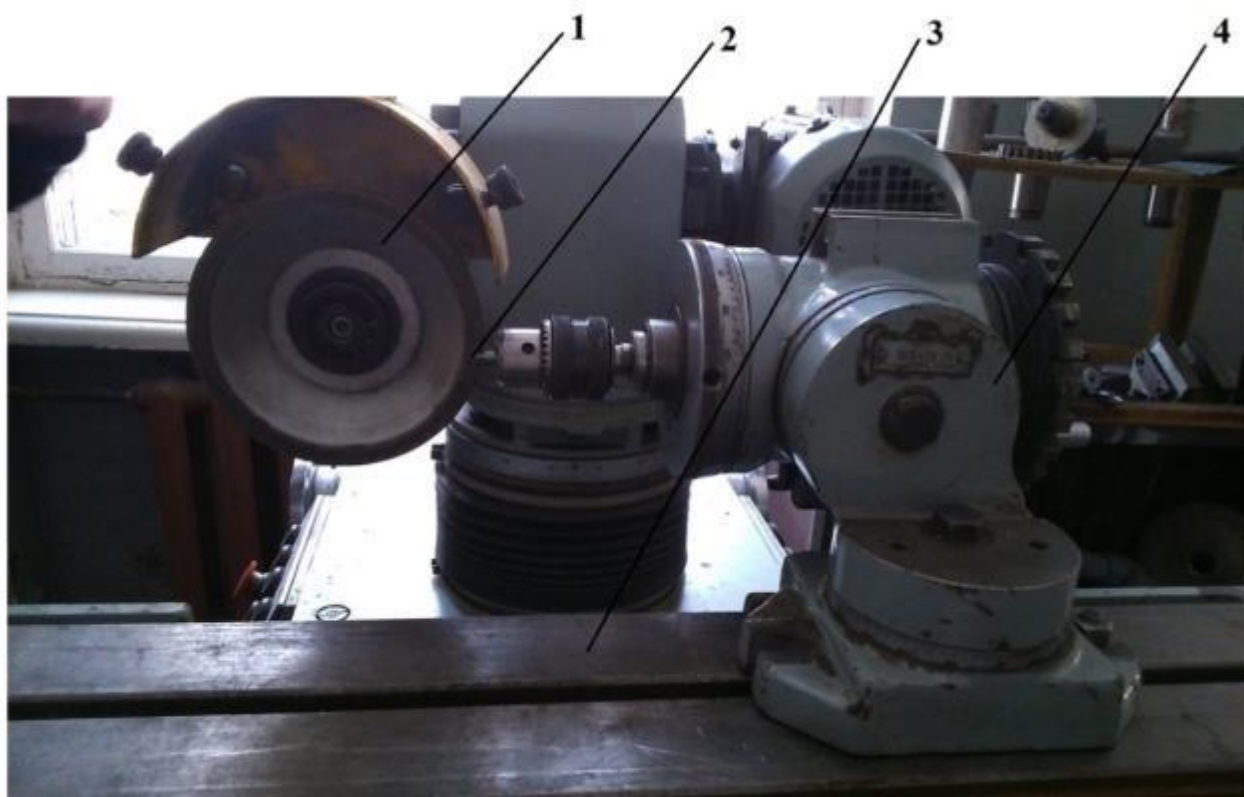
Станок ЗЕ642А: 1 - шлифовальный круг; 2 - заготовка; 3 –стол для перемещения; 4 - приспособление для заточки инструмента;
